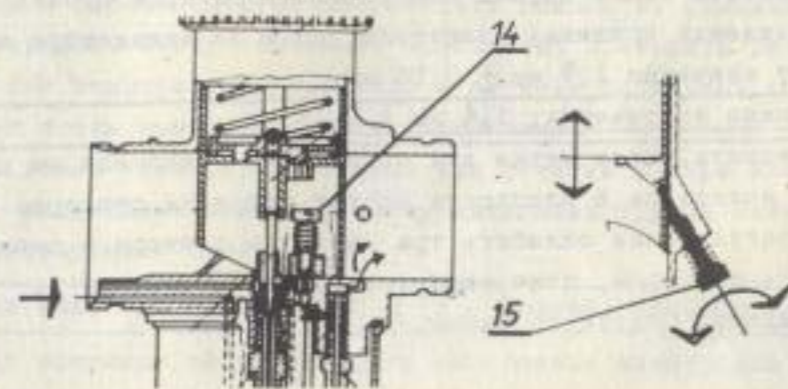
Регулировочный винт карбюратора - гибкий трос газа - рычаг управления дросселем
